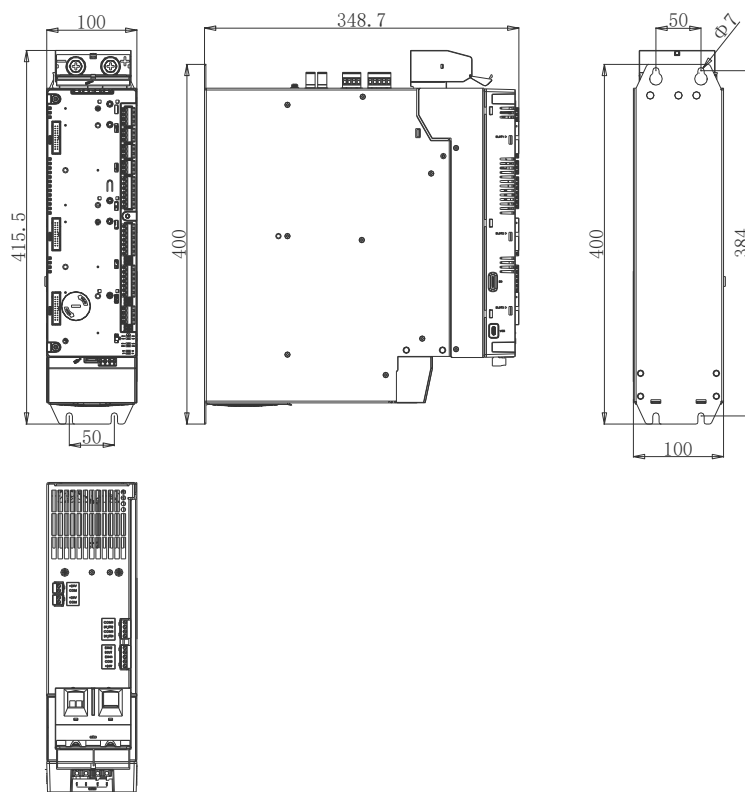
Габаритные размеры инвертора корпуса FR2 (мм)
